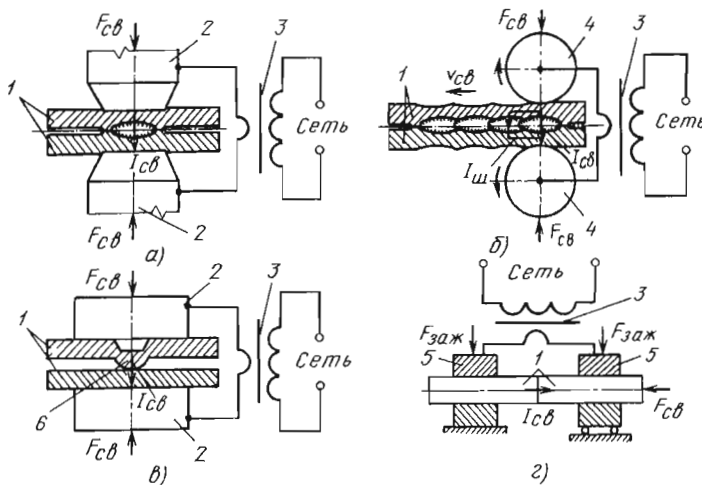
Схемы основных способов контактной сварки:
